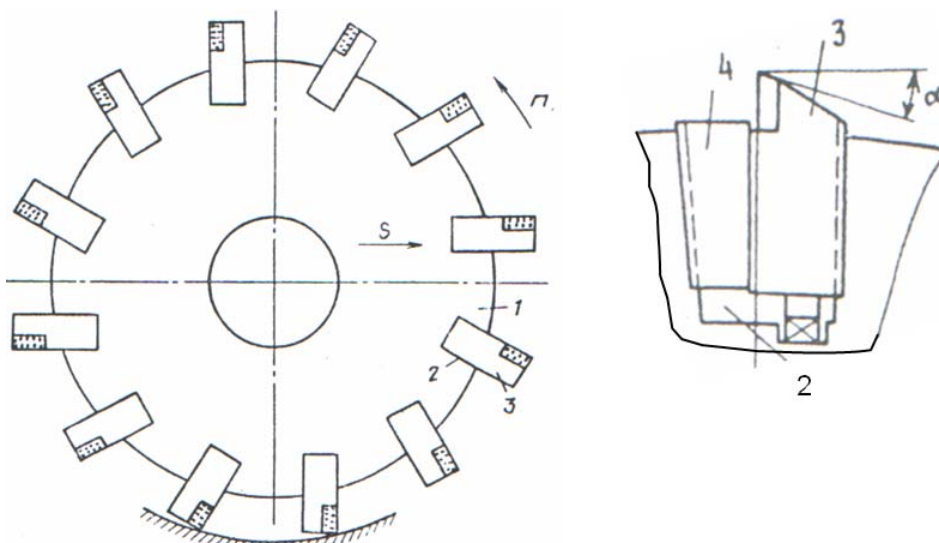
Дисковая фреза 1 со вставными ножами 3 с напайными пластинами из твердого сплава и их крепление в пазу 2 дополнительным клином 4 с рифлениями
